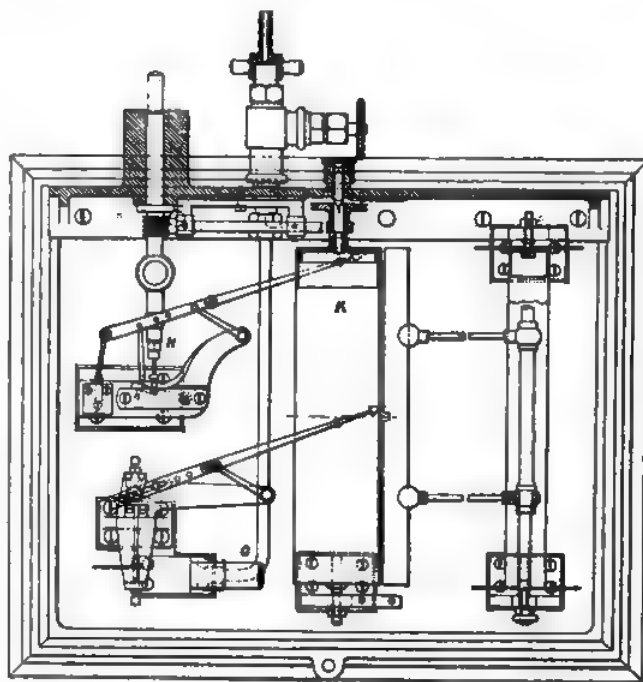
Grundriss der Registrier-Apparate.
